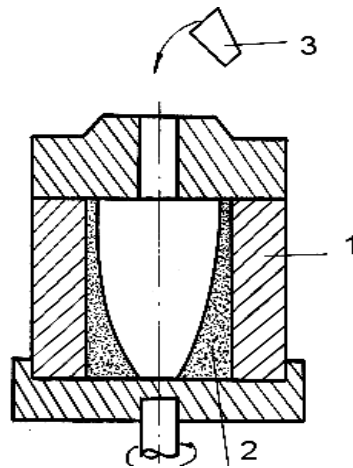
Форма виливки при литті на відцентрових машинах з вертикальною віссю: 1-металева форма; 2-розплавлений метал; 3-тигель
